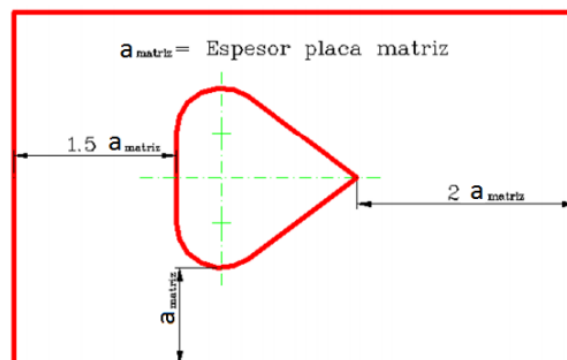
Dimensiones exteriores de la placa matriz. Fuente: [2]
